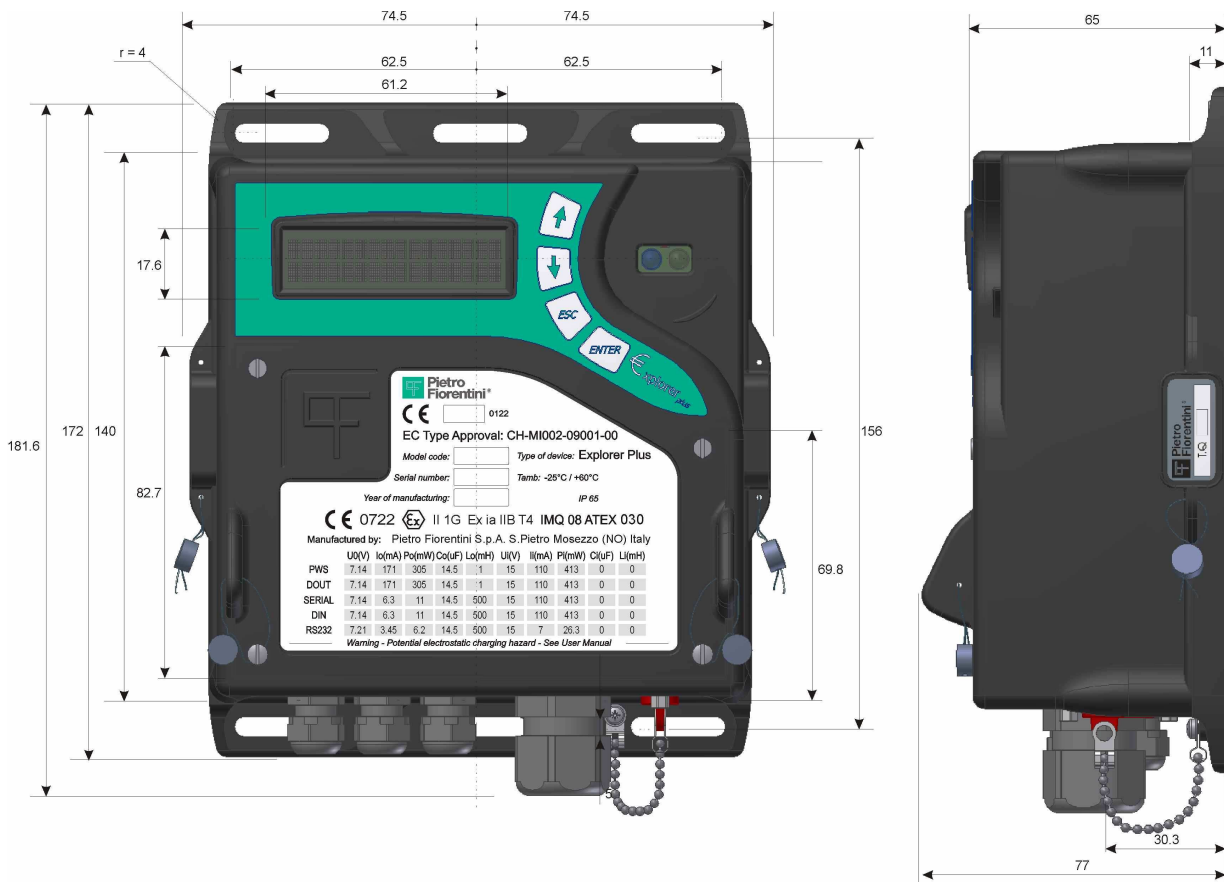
Quote di ingombro apparato e punti di fissaggio
